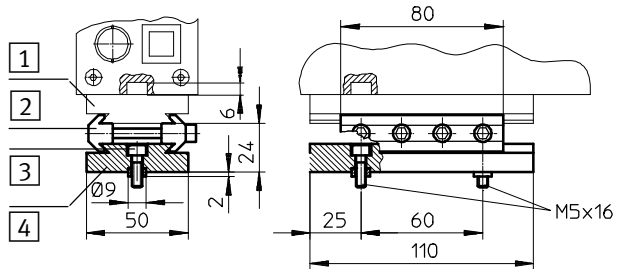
/2: Befestigung der Checkbox mit Verbindungsbausatz HMSV-12
